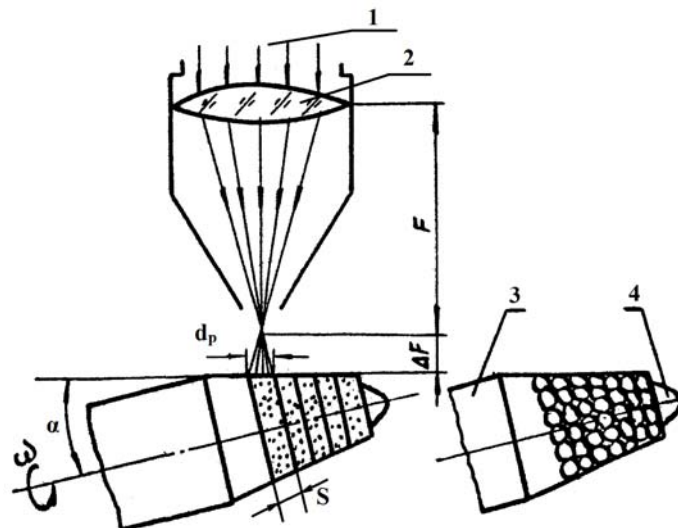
Схеми лазерного зміцнення робочій поверхні державки різця РКС-1 безперервним (а) та імпульсним (б) випромінюванням: 1 – лазерний випромінювач; 2 – лінза; 3 – державка різця; 4 – твёрдосплавна вставка (ВК)
